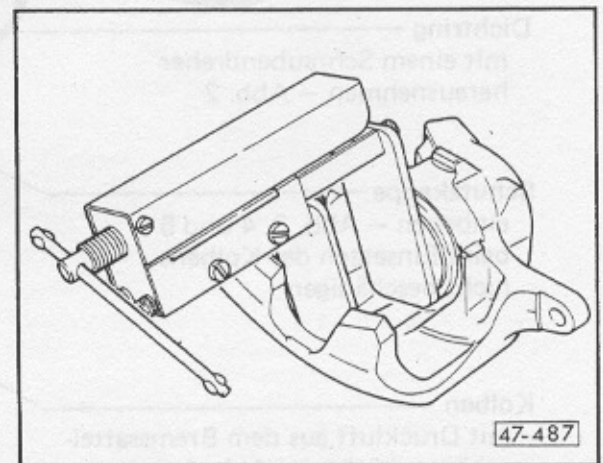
Kolben mit Kolbenrücksetzvorrichtung in den Zylinder drücken.
